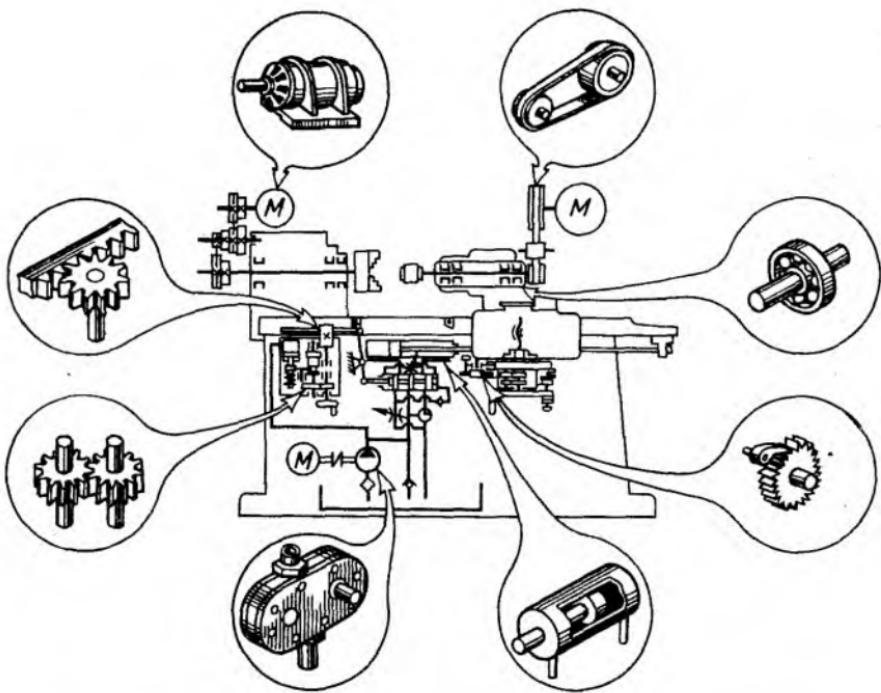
Гидрокинематическая схема внутришлифовального станка
